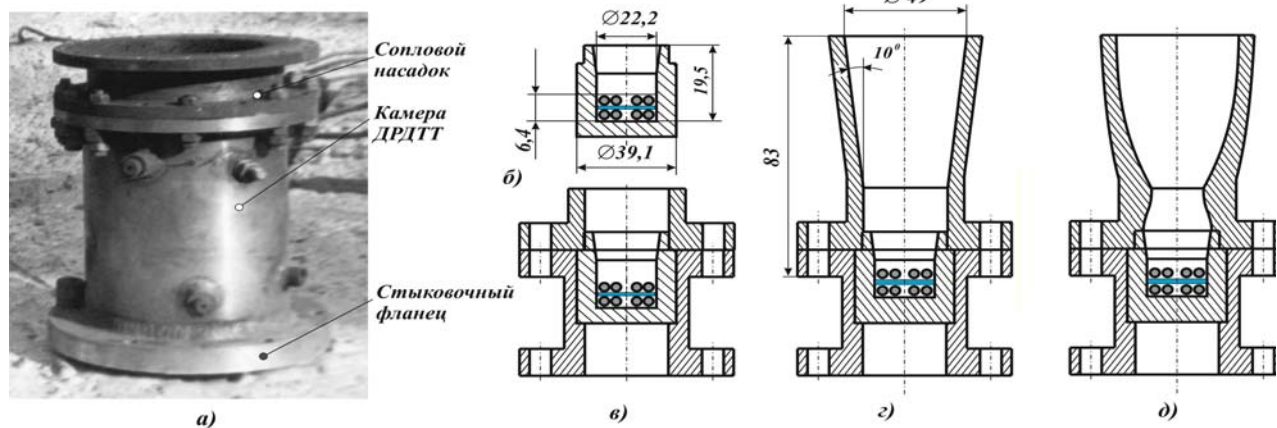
ДРДТ с цилиндрической камерой сгорания и сопловыми насадками:
